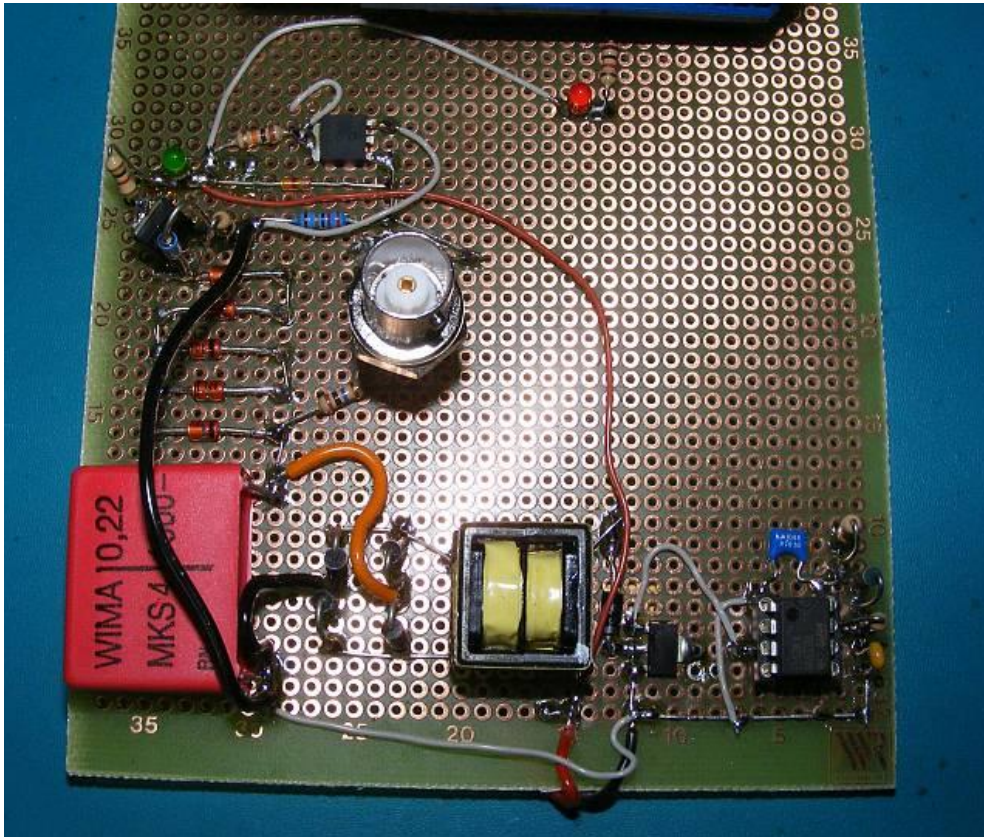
Prototypenschaltung des Geigerzählers auf einer Lochrasterplatine. Die BNC Buchse dient dem Anschluss des über ein Kabel abgesetzten Zählrohrs.
